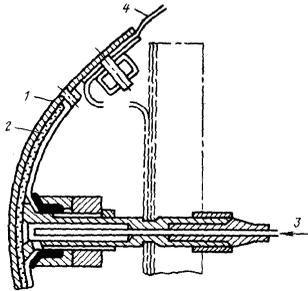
Конструкции рабочей части жидкостной ПОС. 1 – обшивка из пористого металла; 2 – пористый полимерный металл; 3 – подача противообледенительной жидкости; 4 – обшивка носка крыла
